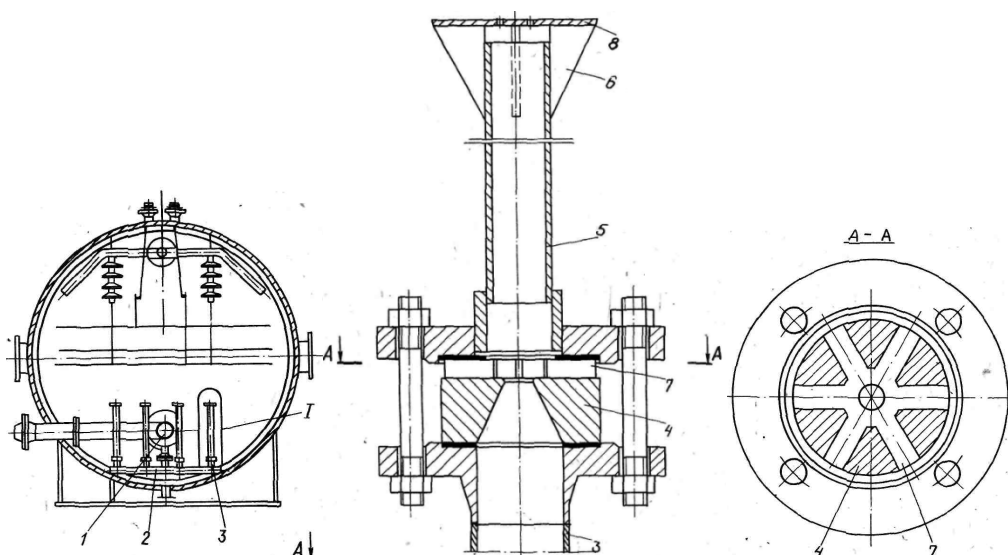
Схема дооборудования горизонтального электродегидратора вертикальными струйными смесителями (1): 1 – продольный коллектор; 2 – поперечный коллектор; 3 – штуцер; 4 – сопло; 5 – смесительный патрубок; 6 – ребро; 7 – паз; 8 – отражатель
